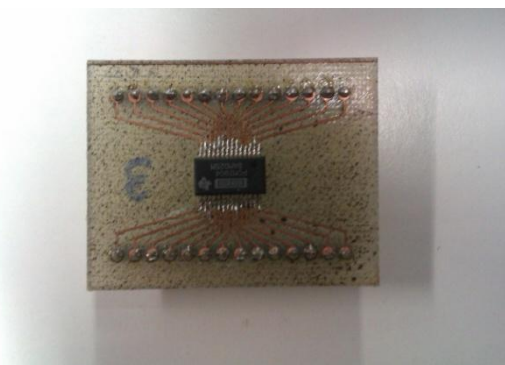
Chip montado en el adaptador para insertarlo en la Protoboard.
